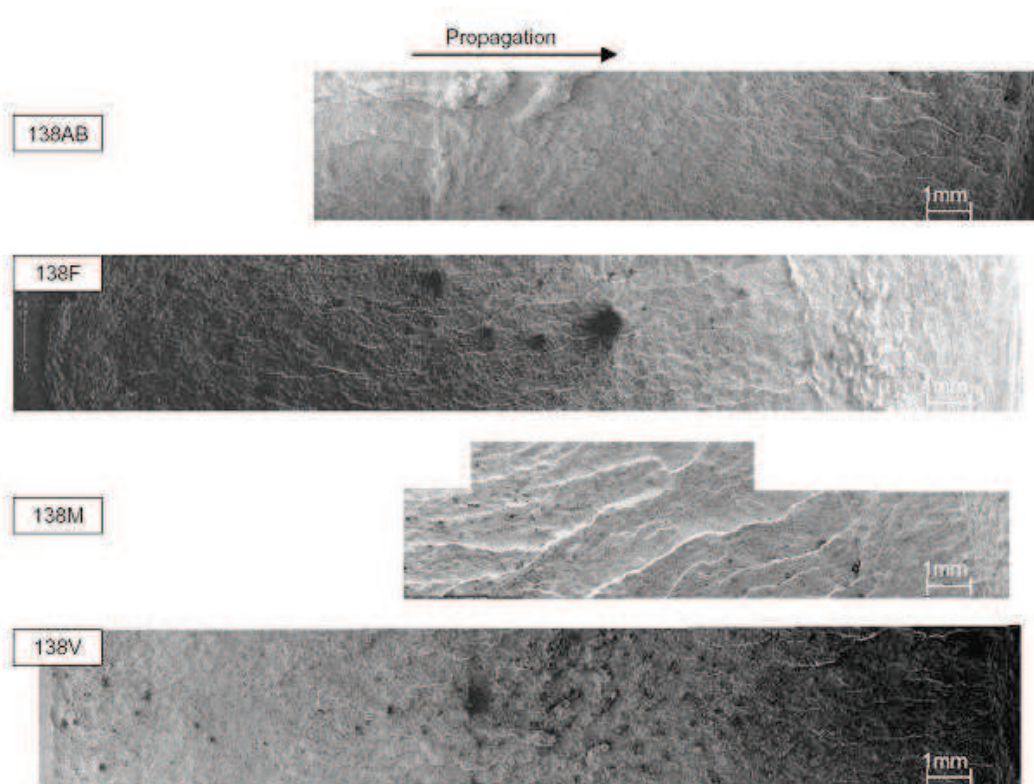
Fractographies des propagations de fissure - éprouvettes CT testées à -150°C
